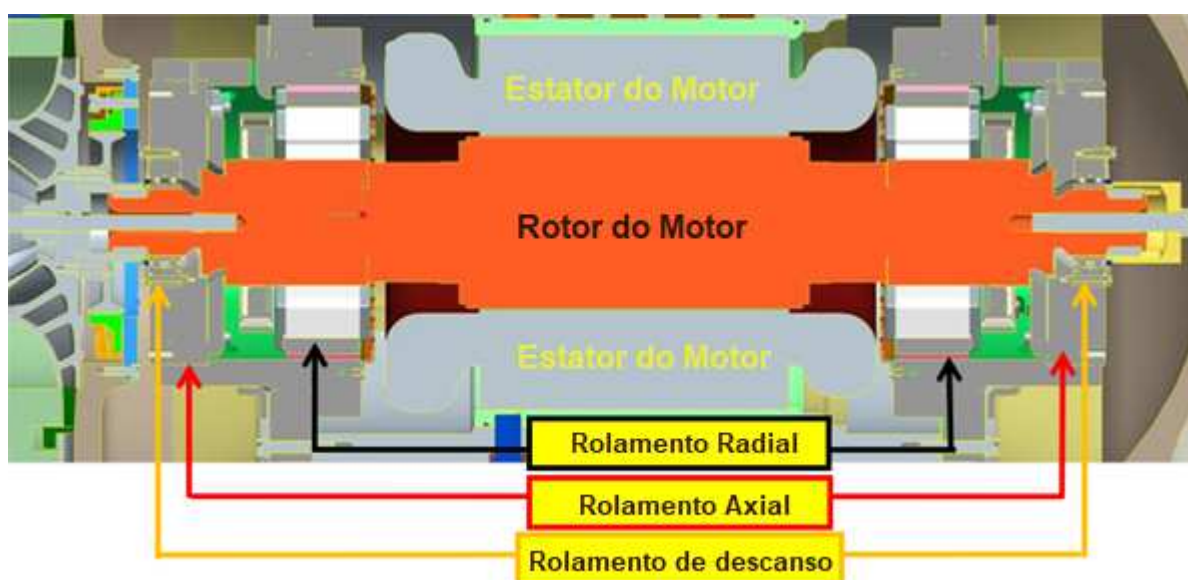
Vista em corte frontal do motor do mancal magnético
